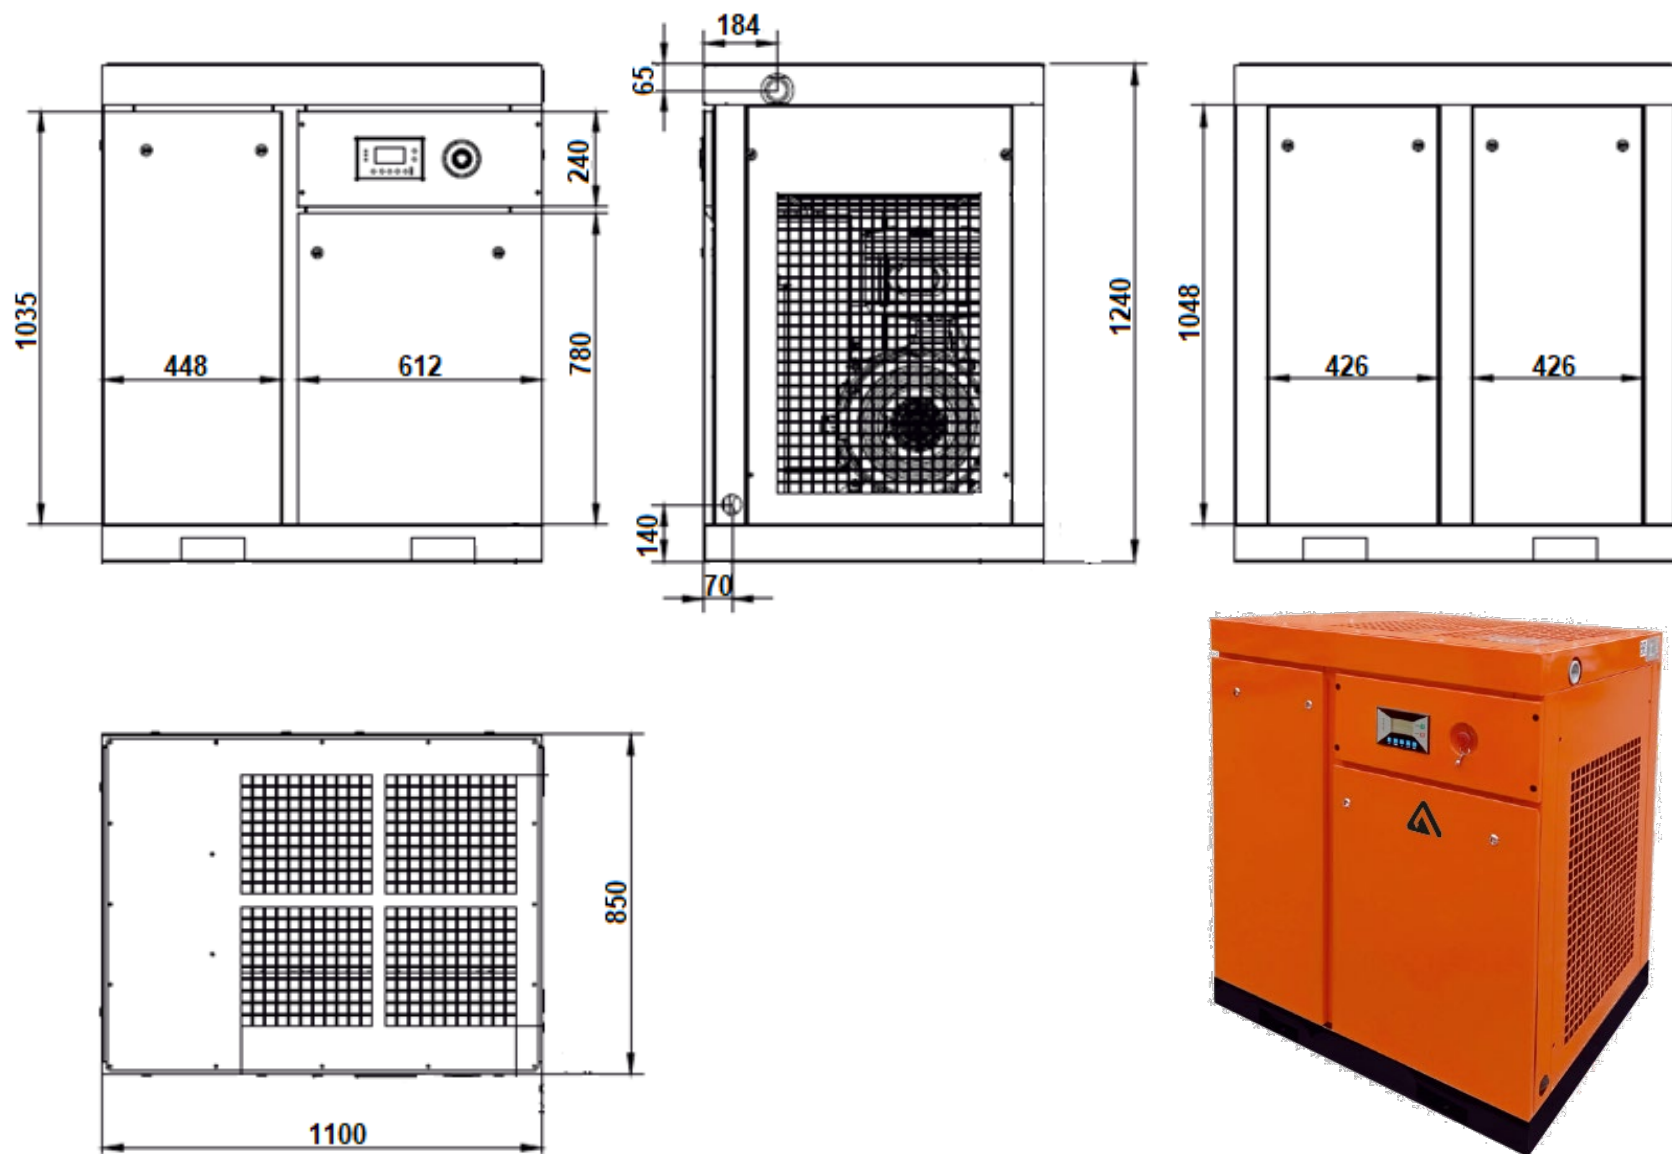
Общий вид, габаритные размеры станции компрессорной ЗИФ-СВЭ типа АРМ с двигателем 30 кВт
